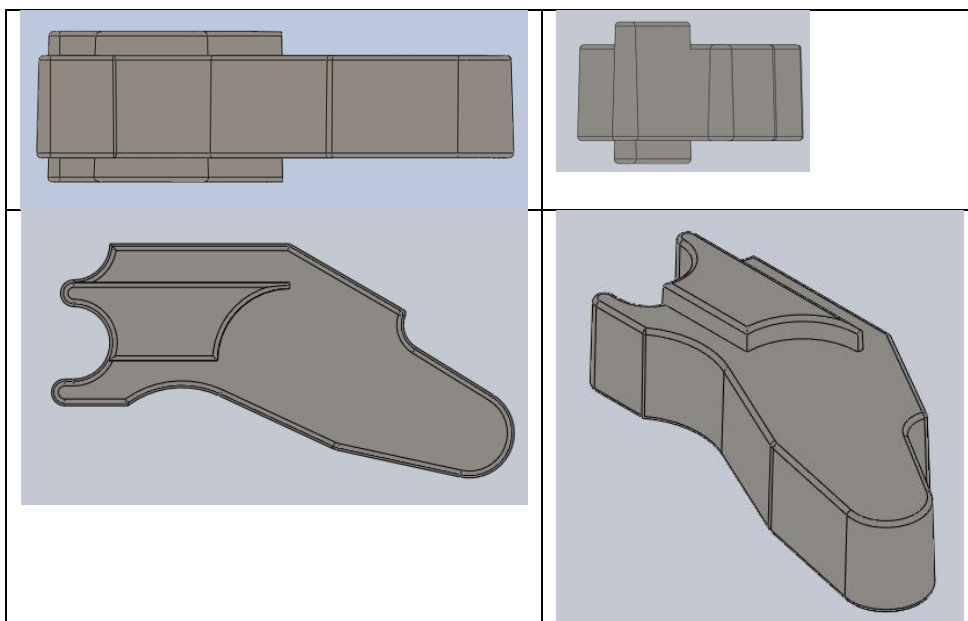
Компьютерная объемная модель заготовки детали «Рычаг»
